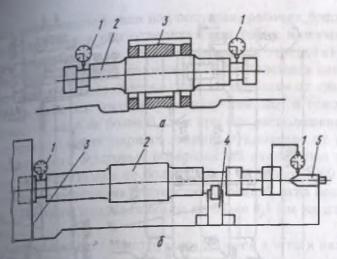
Выверка положения вала при сверлении глубокого отверстия
